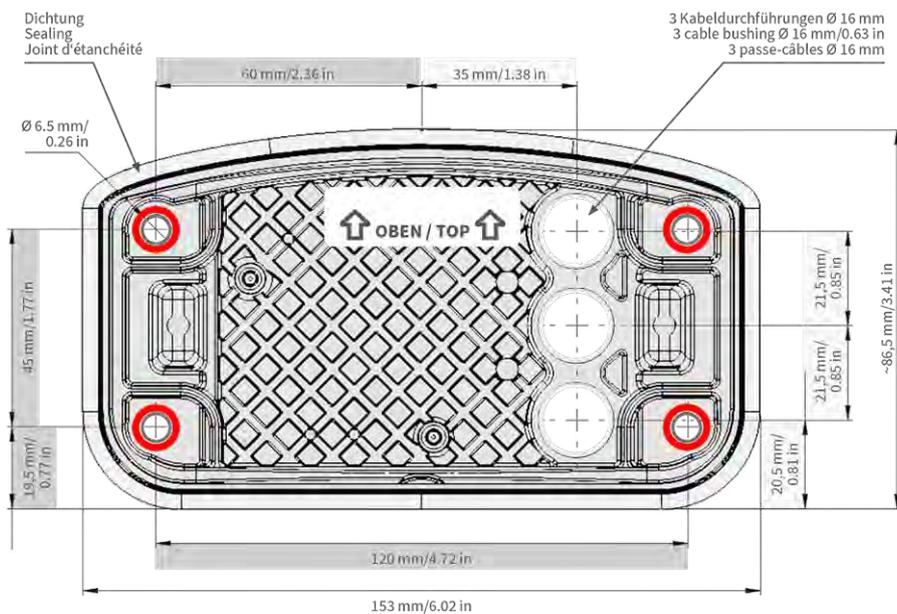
Montageplatte mit markierten Bohrungen für Befestigungsschrauben
